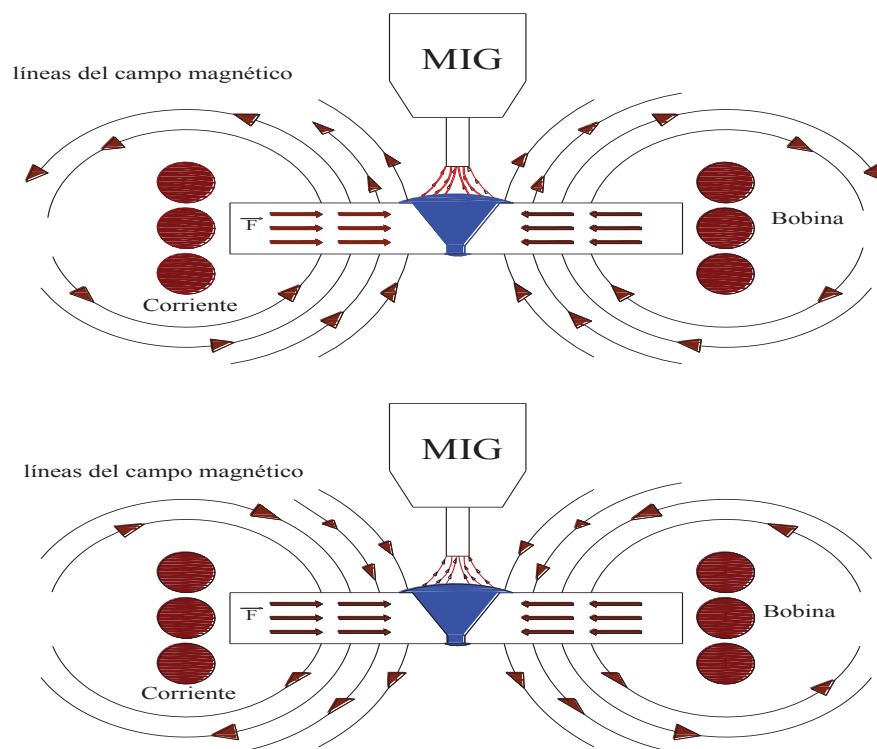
Representación esquemática de la aplicación del campo magnético y su interacción con el campo generado por la corriente (CD) del proceso de soldadura.
